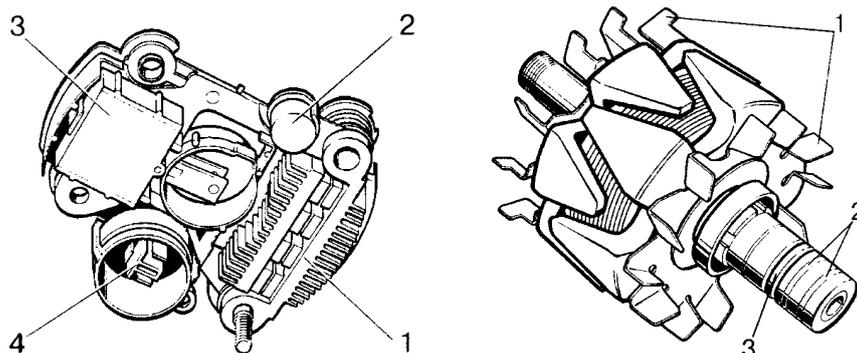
Объединенный узел "выпрямитель, регулятор напряжения, щеткодержатель" генераторов фирмы Mitsubishi: 1 - выпрямитель; 2 - помехоподавительный конденсатор, 3 - регулятор напряжения с щеткодержателем; 4 - колодка со штекерными выводами L. O.C. S
